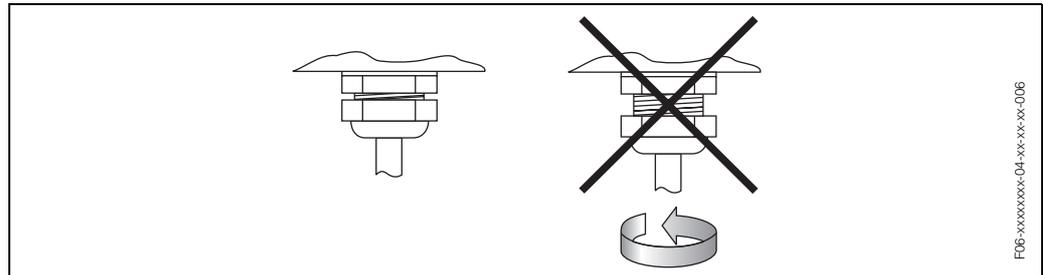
Instrucciones de instalación referentes a las entradas de cables de la caja del transmisor
